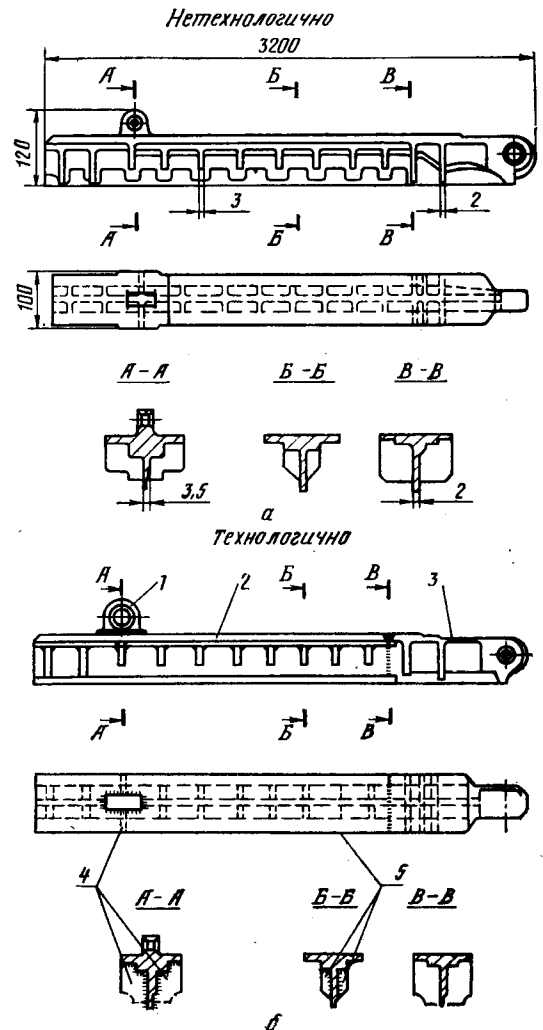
Монолитная (а) и сварная (б) конструкции балок.
